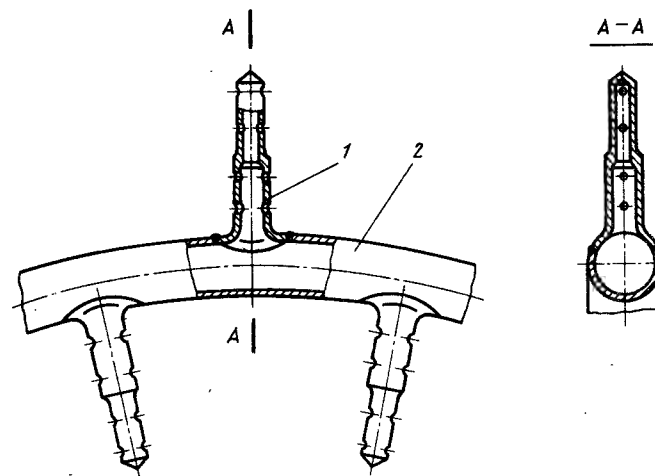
Коллектор со струйными форсунками-распылителями: 1 — форсунка-распылитель; 2 — коллектор
